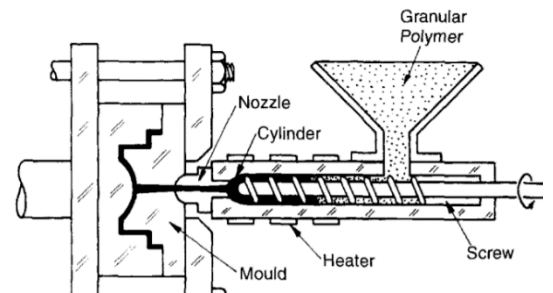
Moldeo por inyección. Un polímero granular es calentado, comprimido y cortado por un alimentador de tornillo, forzado en una cavidad del molde [22].
